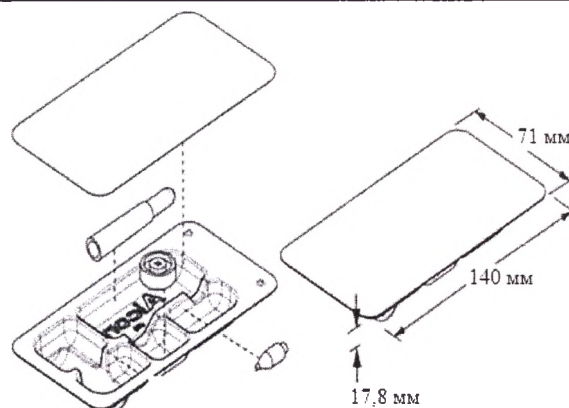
Стерильная упаковка для мелких деталей с размерами.
